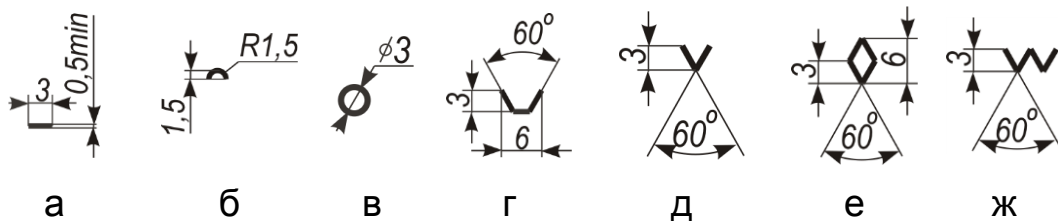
Позначення форми робочої поверхні: а – плоска; б – сферична; в – циліндрична; г – призматична; д – конічна; е – ромбічна; ж – рельєфна
